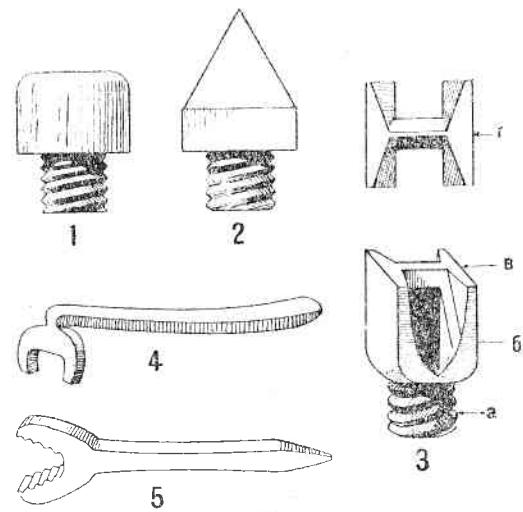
Шипы и принадлежности к ним. 1 — тупой винтовой шип; 2 — винтовой острый шип; 3 — винтовой шип Нейса, вид снизу и сбоку; 4 — Лапа для удержания подковы при ввинчивании шипа; 5 — ключ.
